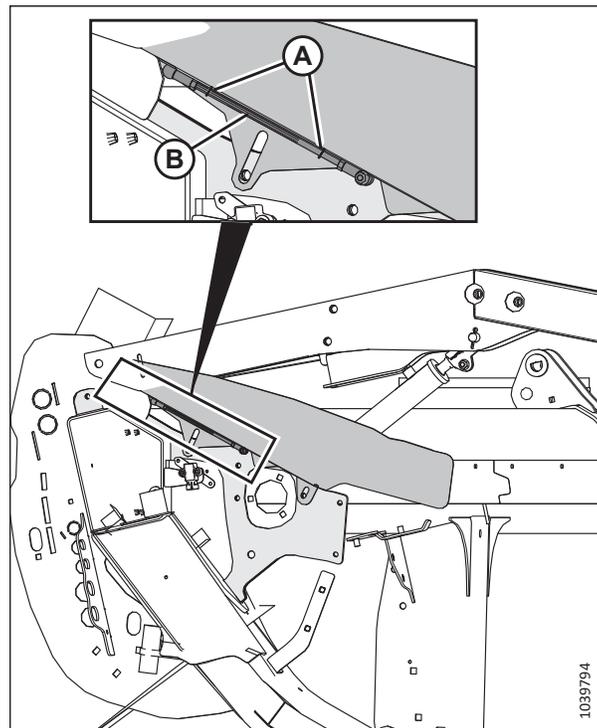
Emplacement du capteur de hauteur du rabatteur
